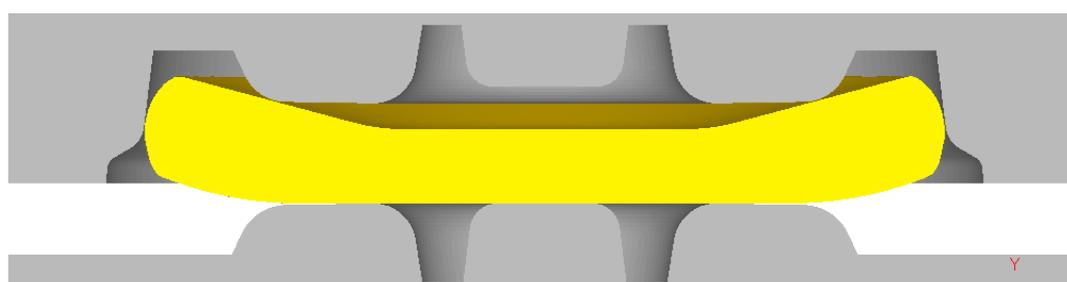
Штамповка колёсной заготовки по схеме Б:
